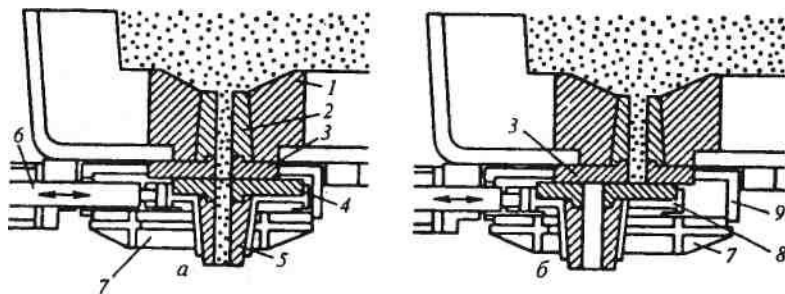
Шиберный затвор в открытом (а) и закрытом (б) положении: 1 — гнездовой кирпич; 2 — разливочный стакан; 3 — неподвижная огнеупорная плита; 4 — подвижная огнеупорная плита; 5 — стакан-коллектор; 6 — шток гидроцилиндра; 7 — направляющая рамка; 8 — подвижный шибер; 9 — неподвижный корпус
